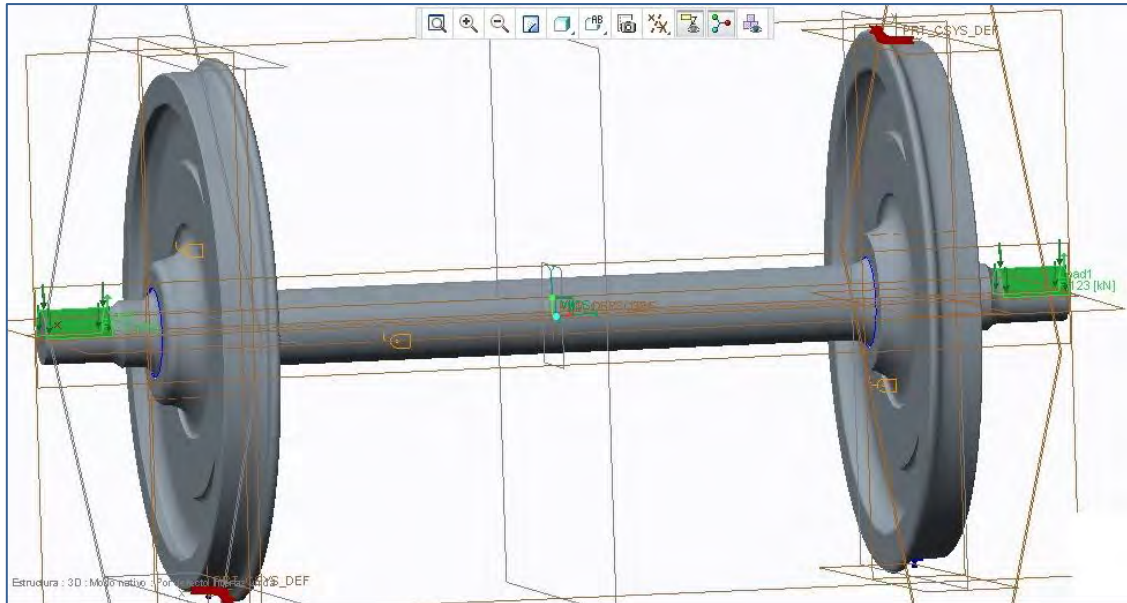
6. Conjunto modelado con restricciones en elipses de apoyo y carga sobre las manguetas
